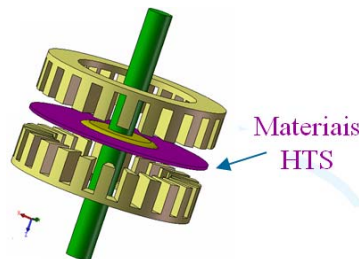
Desenho do motor em disco com rotor em materiais supercondutores (SAT).
